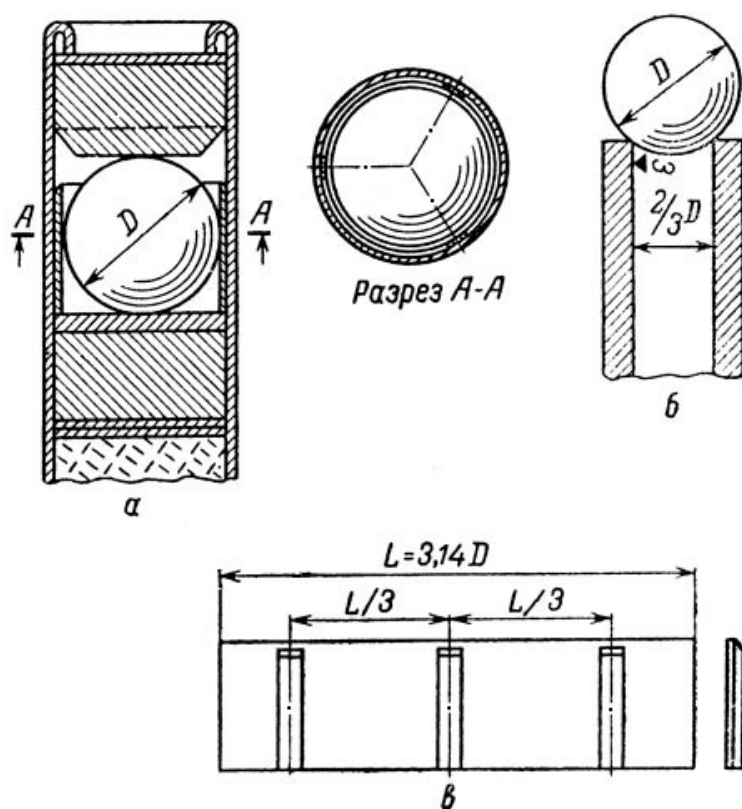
Схематический чертеж снаряжения патронов шаровидной пулей по способу Э.К. Келера: а — общий вид патрона; б — металлическая трубка для обтачивания пули по диаметру ствола в дульном сужении; в — приспособление для центрирования пули
